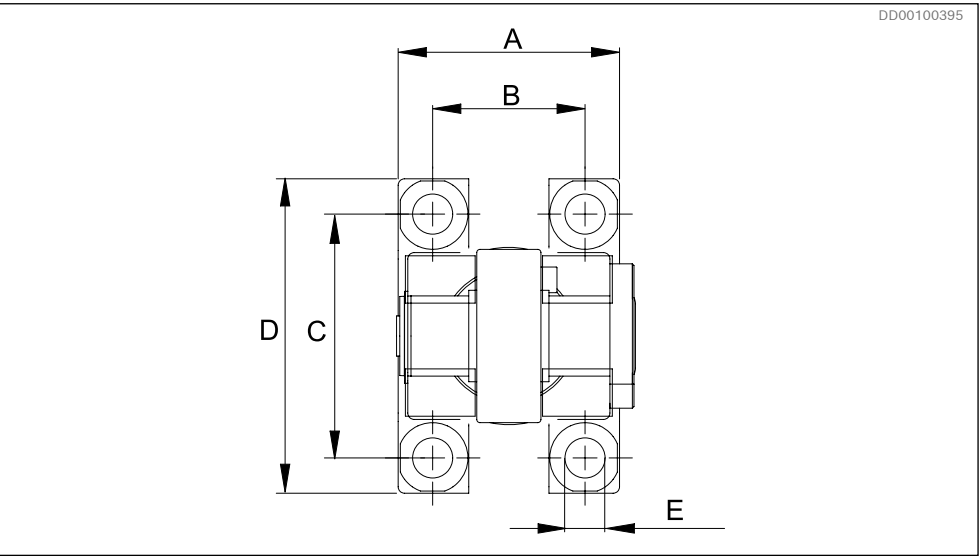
Расположение отверстий для шарнирного соединения и гидравлического цилиндра для DTCB
